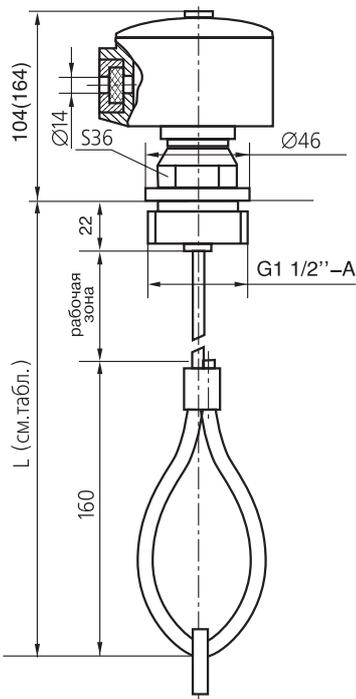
Общий вид, габаритные и установочные размеры СУС 191Р(Б)
